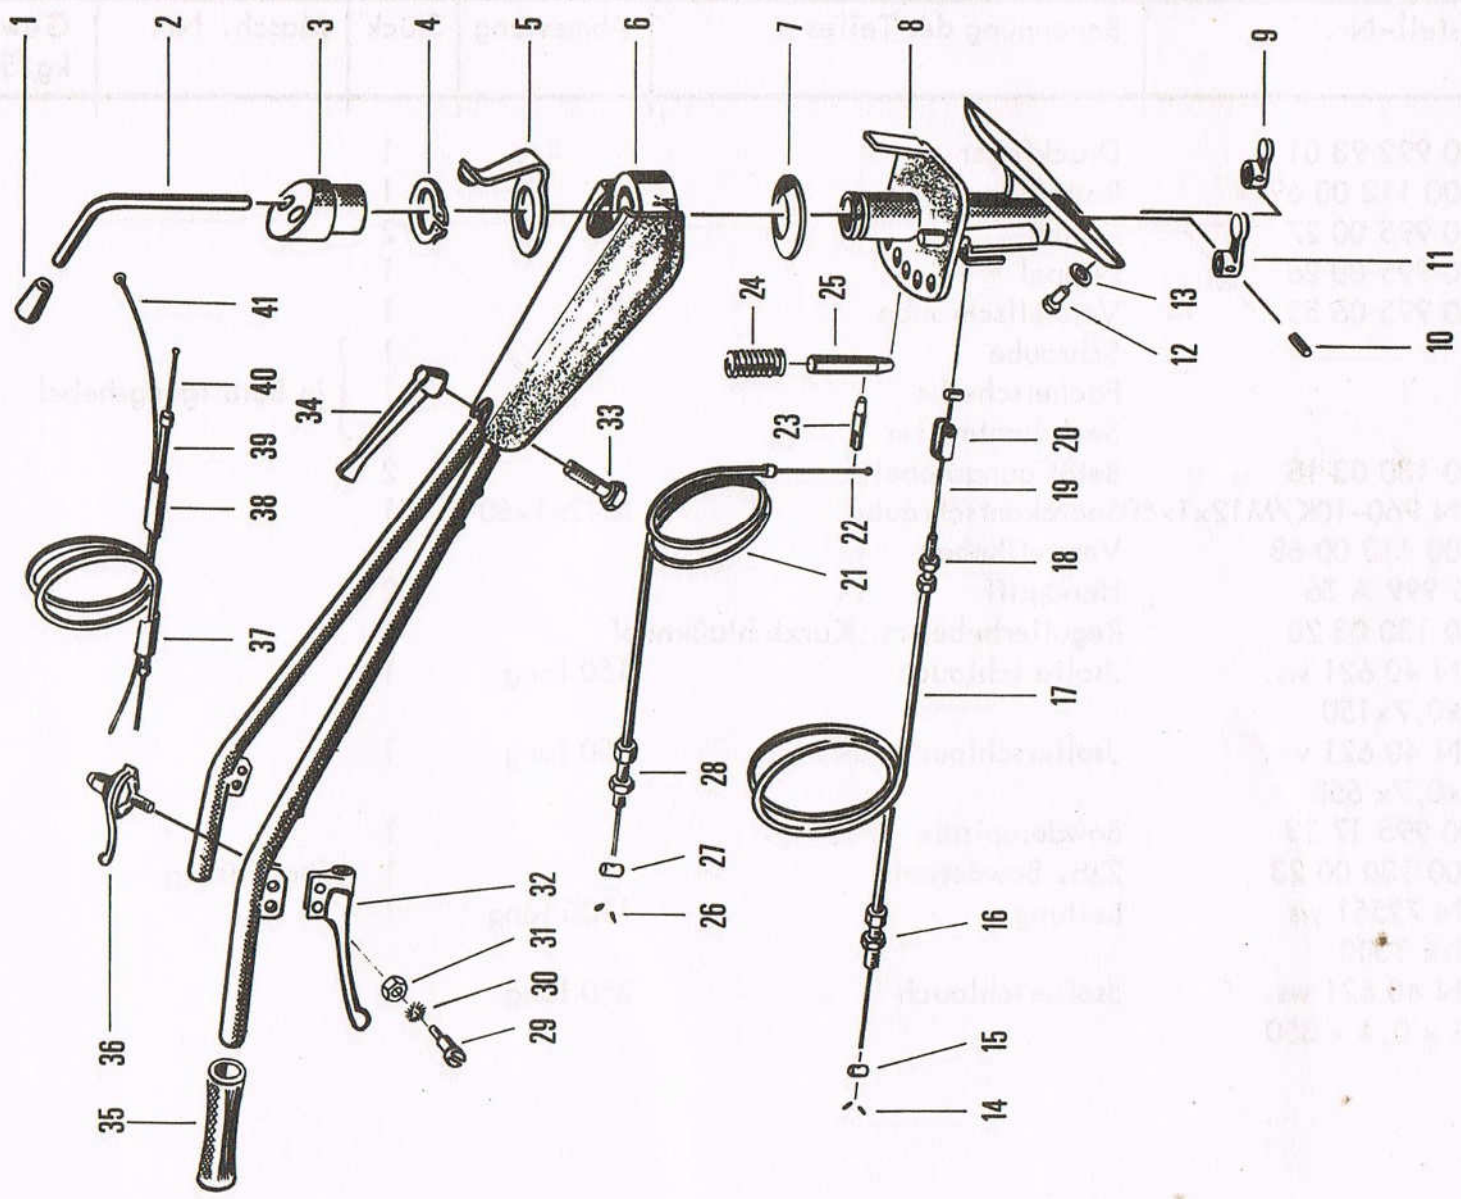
FRONTTRIEBRAD - STÜTZE - MOTOR
